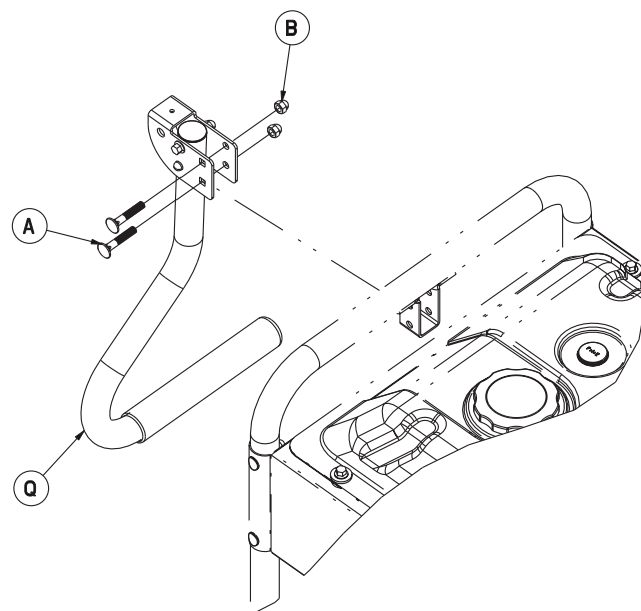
В. Сборка ручки/Сборка ножи (GP2600)
